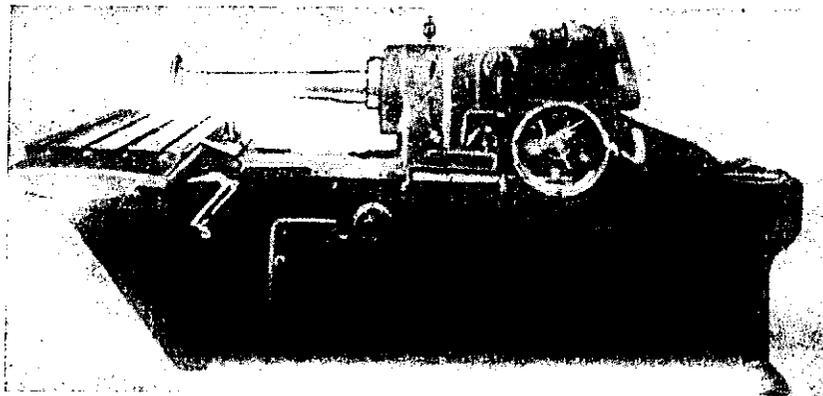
Станок для шлифовки зеркала цилиндров с планетарным движением камня.
